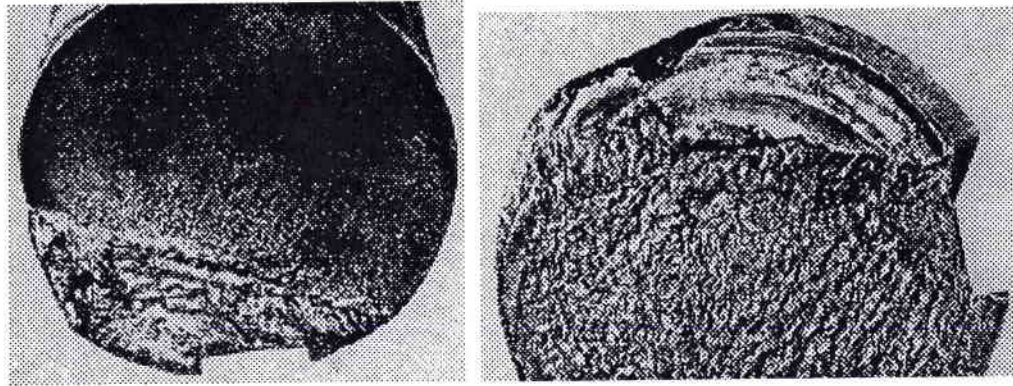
Exemples de rupture par fatigue des arbres clavetés soumis à un chargement de flexion.
